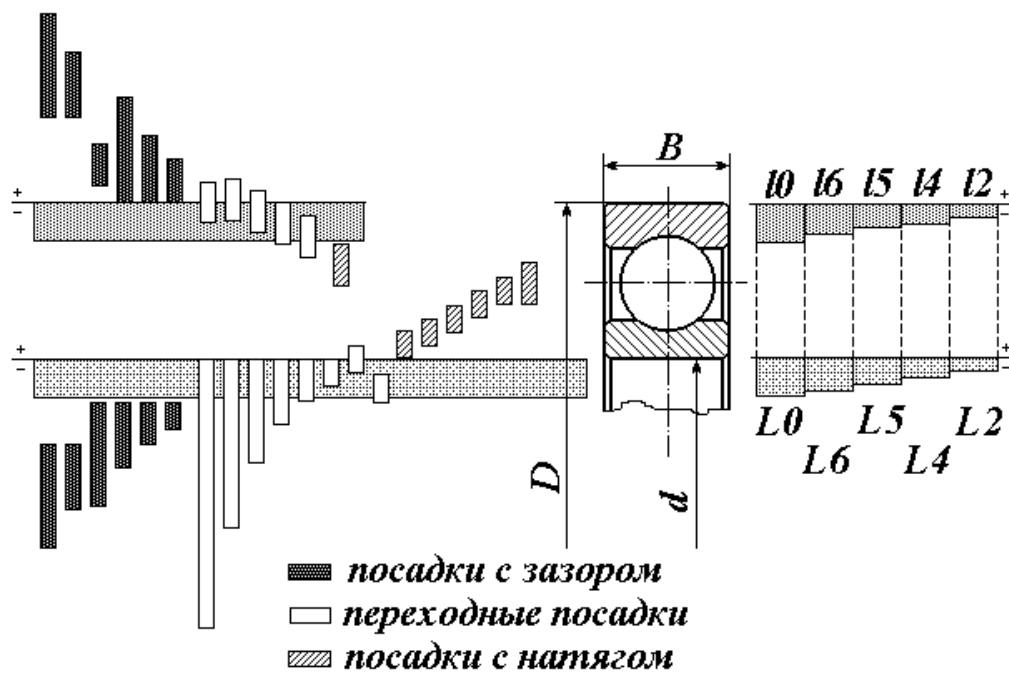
Схема расположения полей допусков для посадочных диаметров подшипника и сопрягаемых с ними поверхностей (вал и корпус)
